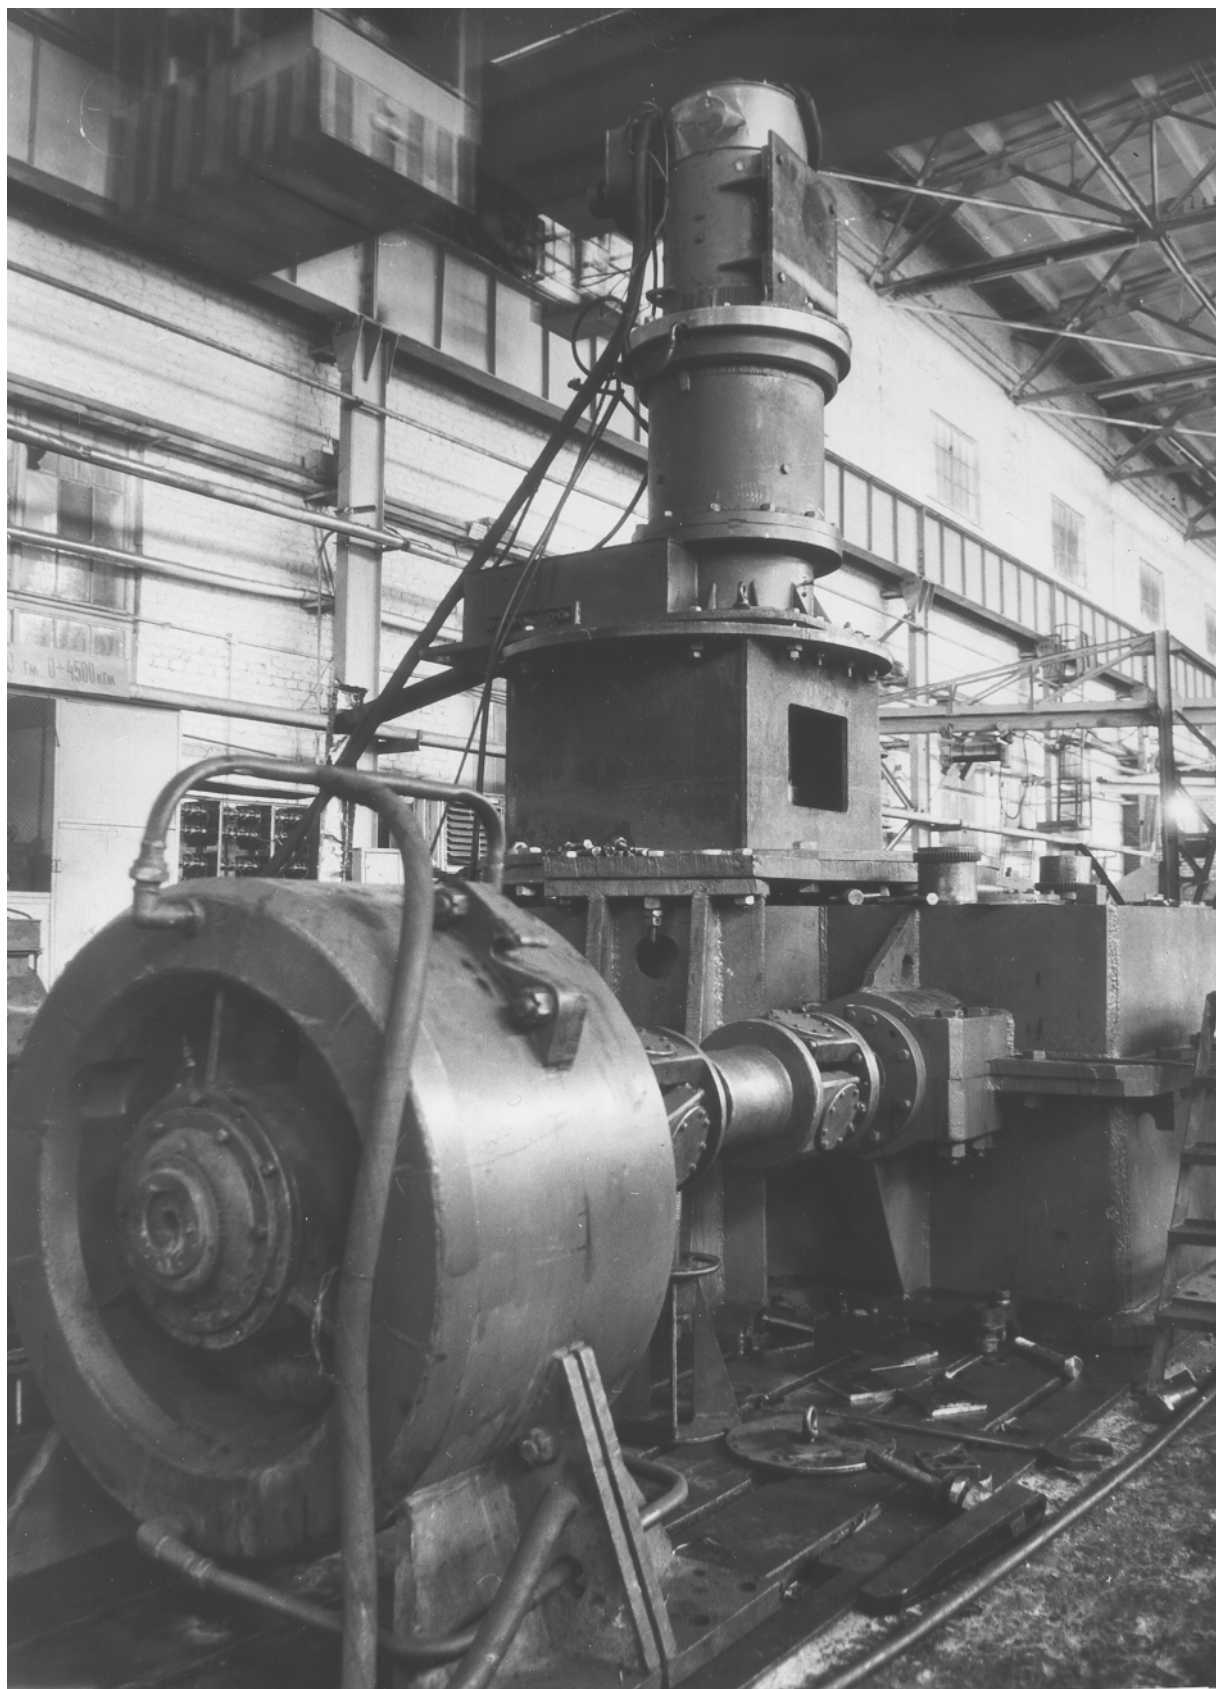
Стенд для испытания вертикальных редукторов с промежуточными телами качения ПК-500 механизма поворота шагающего экскаватора ЭШ6,5×45
